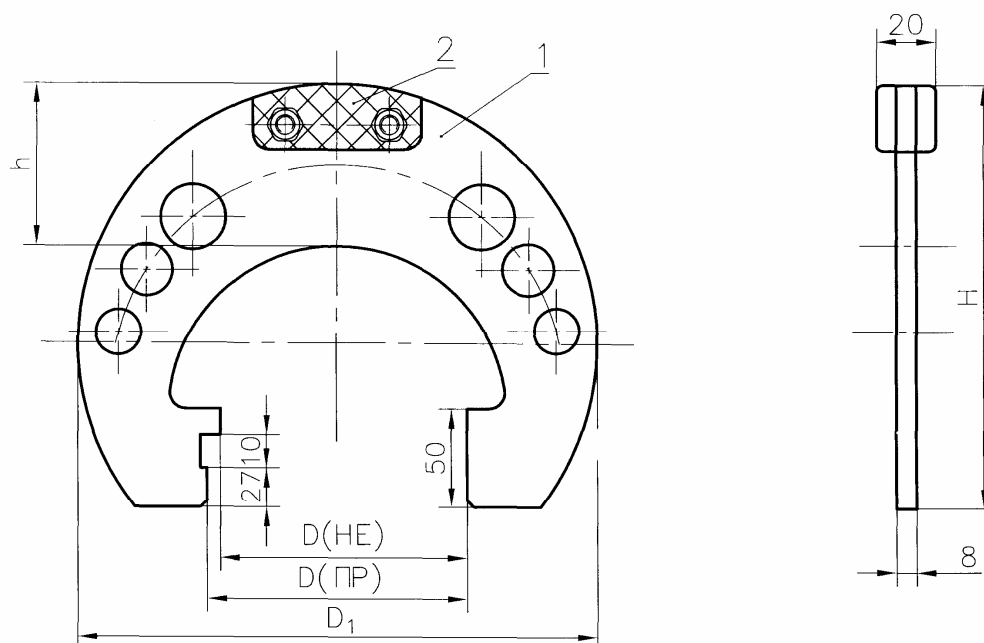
Калибр-скоба односторонний двупредельный:
